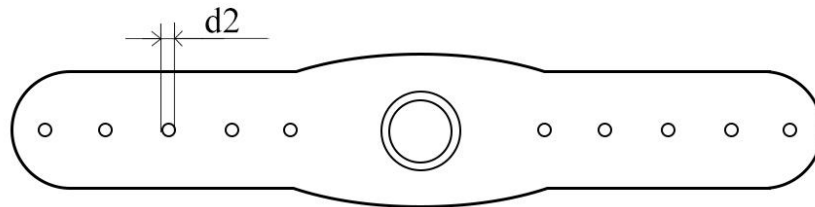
Схематичное изображение коромысла с обозначением диаметра отверстий
